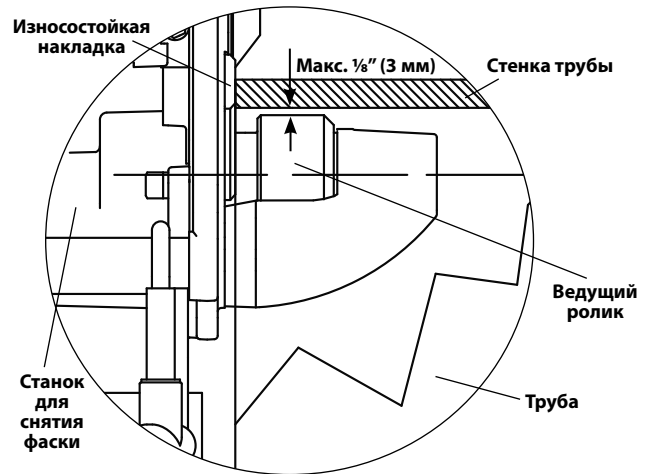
Закрепленный станок для снятия фаски, расположение трубы относительно ведущего ролика станка (обрезная труба - перед захватом)
